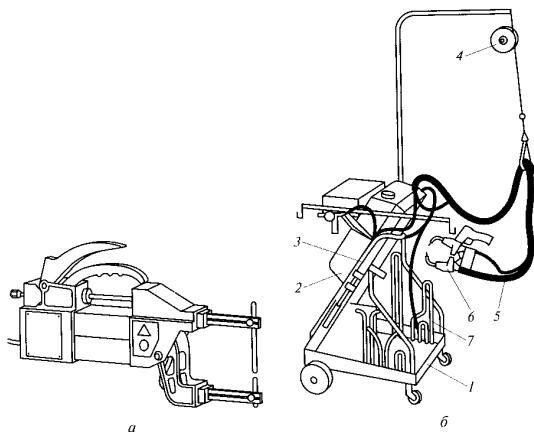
Сварочные клещи (а) и универсальный аппарат контактной сварки (б): 1 – тележка; 2 – внешний источник тока; 3 – споттер; 4 – балансир; 5 – гибкий кабель; 6 – сварочные клещи; 7 – сменные электроды
